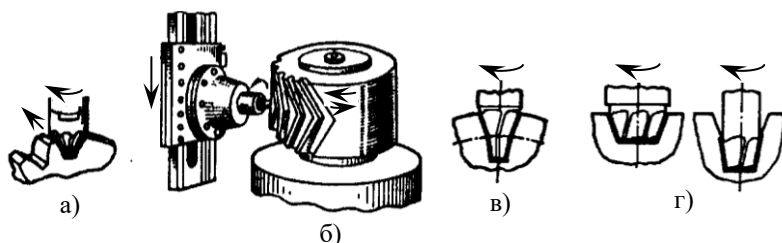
Нарізання зубів зубчастих коліс пальцевими фрезами:
